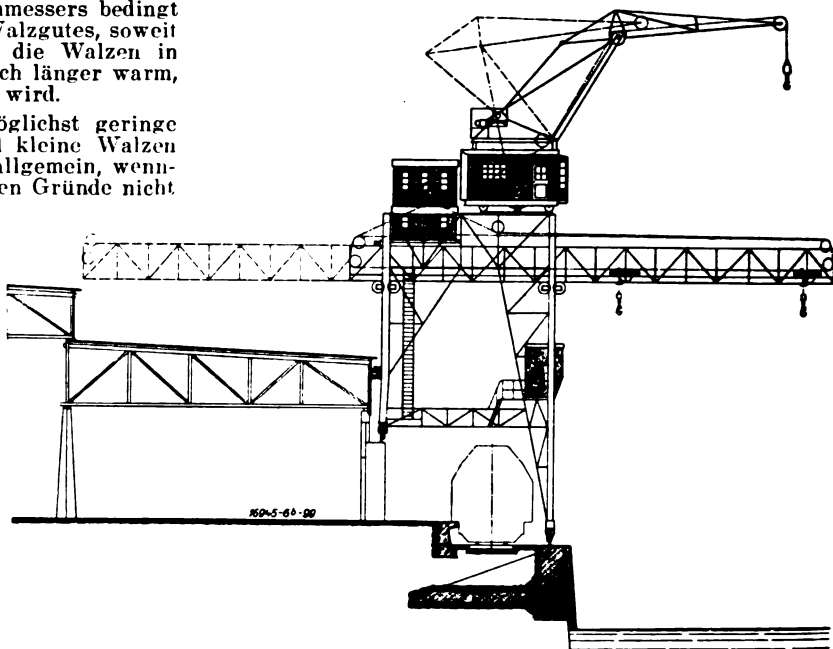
Schema eines Dreifachkrans, Drehkran mit Wippausleger ausgerüstet.
